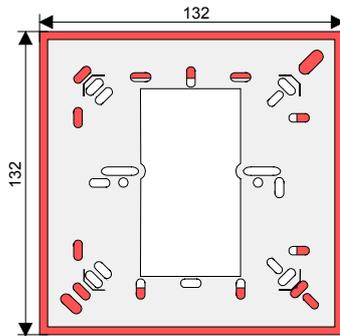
Cadre de montage universel pour fixation au mur (Réf. 704967)
